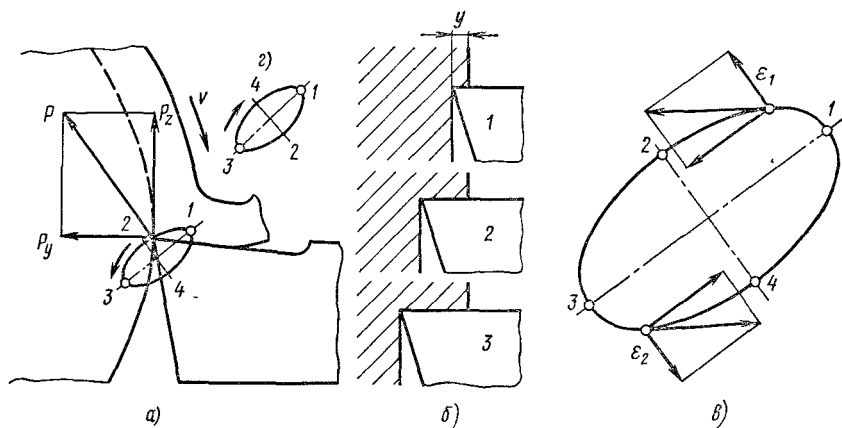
Траектория относительного движения инструмента и заготовки при автоколебании
